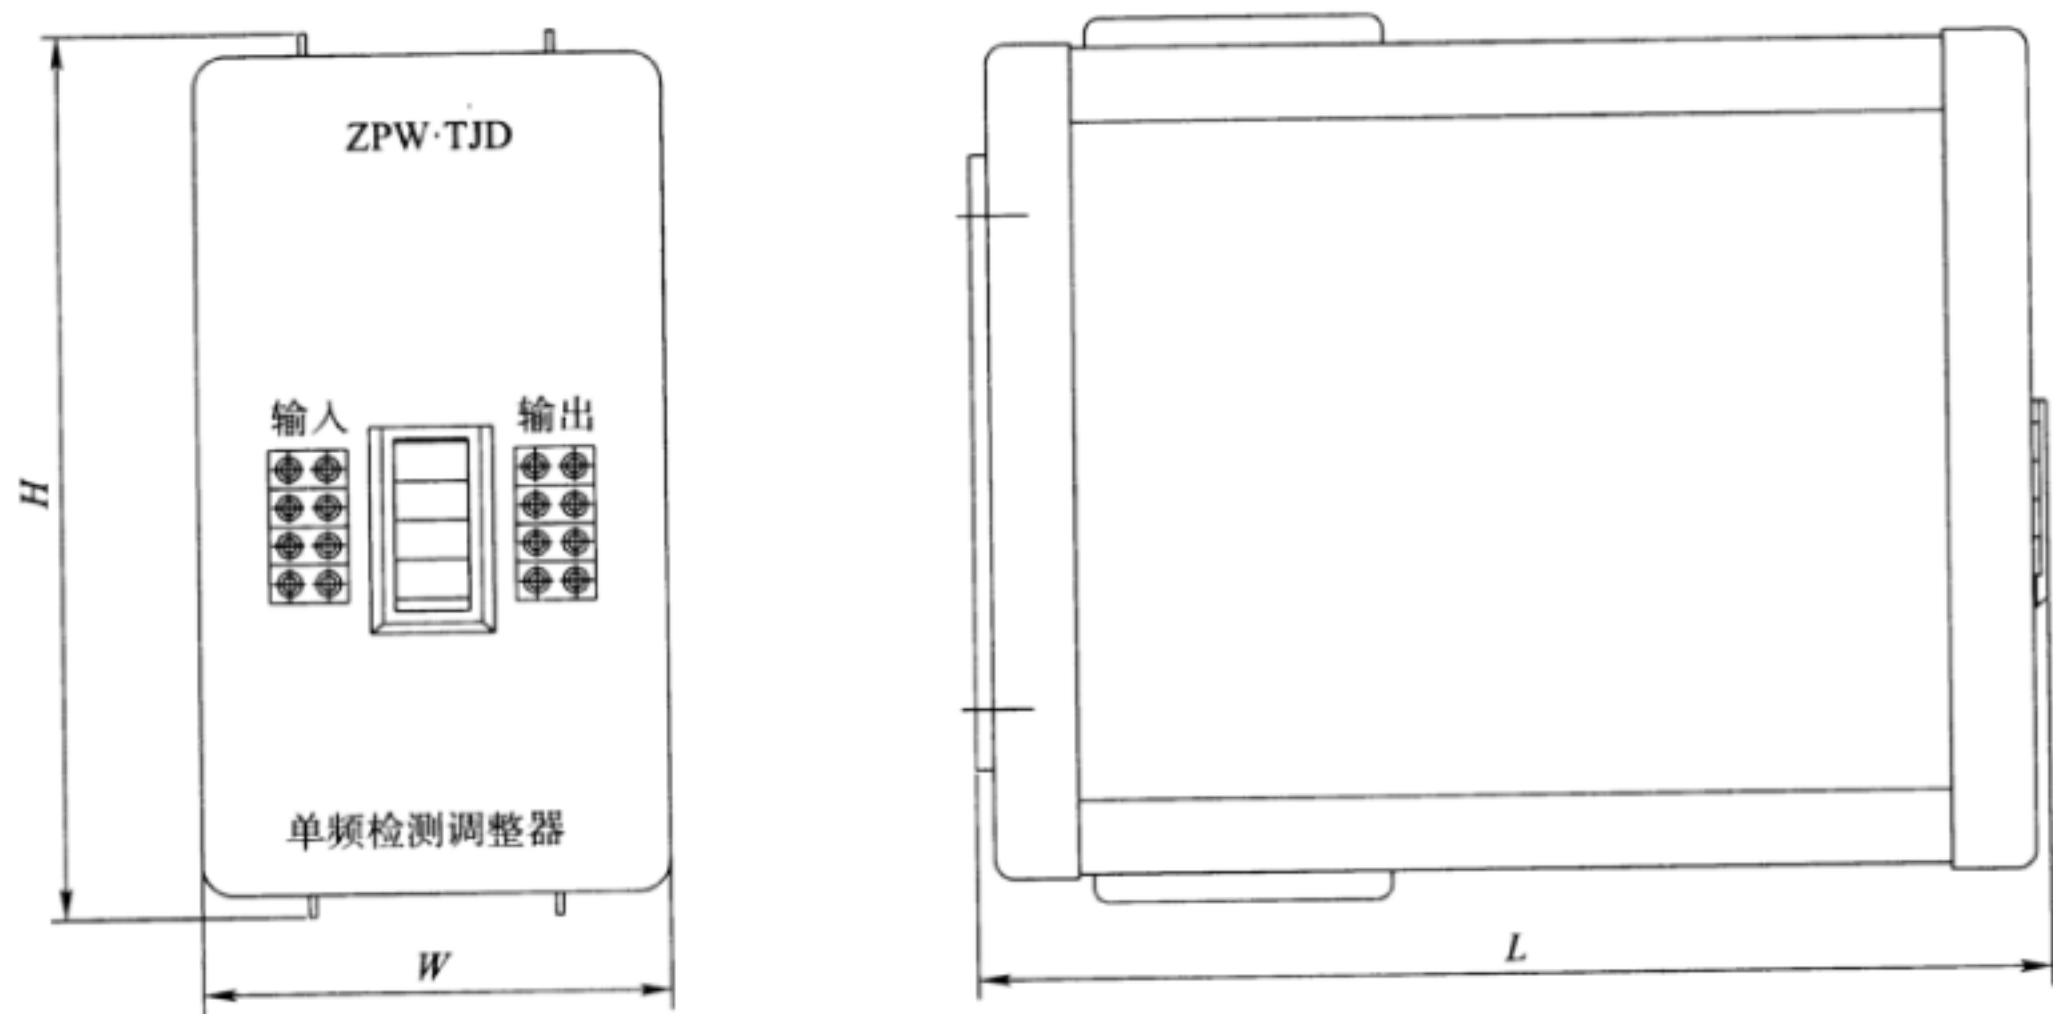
ZPW·TJD 型单频检测调整器外形尺寸
